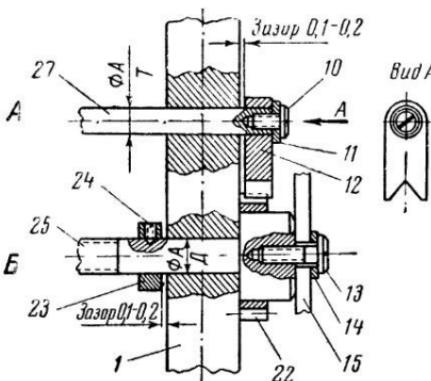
Модель механизма подачи стола поперечно-строгального станка (схема соединения деталей): А — узел крепления собачки храпового механизма (10 — винт, 11 — шайба, 12 — собачка храпового механизма, 27 — направляющая «стола»); Б — узел «ходового винта» (1 — стойка, 13 — винт крепления коромысла, 14 — шайба, 15 — коромысло, 22 — зубчатое колесо храпового механизма, 23 — стопорное кольцо, 24 — стопорный винт, 25 — «ходовой винт»).
